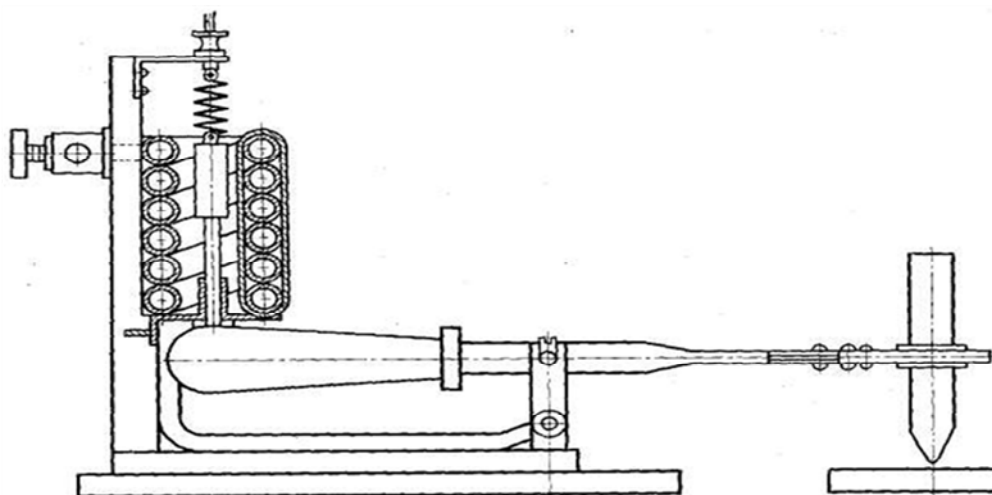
Установка Н. Н. Бенардоса для дуговой сварки с автоматическим регулированием дуги
